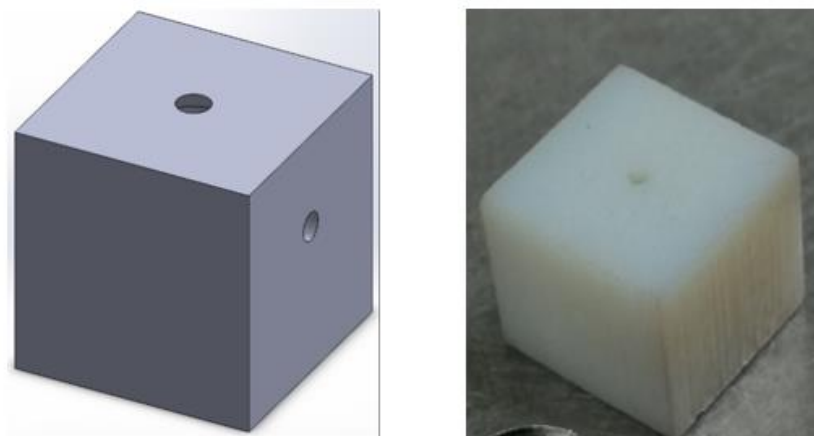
Diseño en CAD 3D de la cavidad y cavidad impresa.
